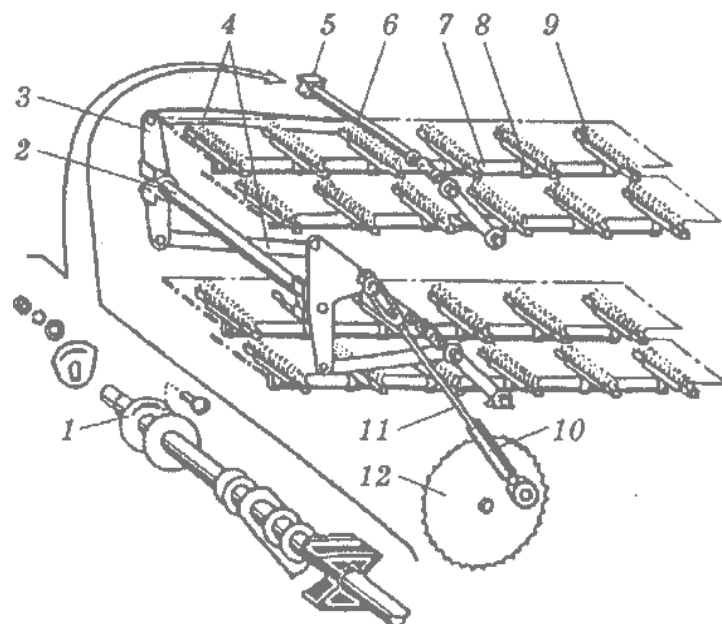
Механізм очищення решіт ОВС-25: 1 - регулятор; 2 - вал приводу щіток; 3 - важелі; 4 - шатуни; 5 - повзуни; 6 - колінчастий вал; 7 - труба; 8 - скоба; 9 - щітка; 10 - демпфер; 11 - водило; 12 - зірочка.
